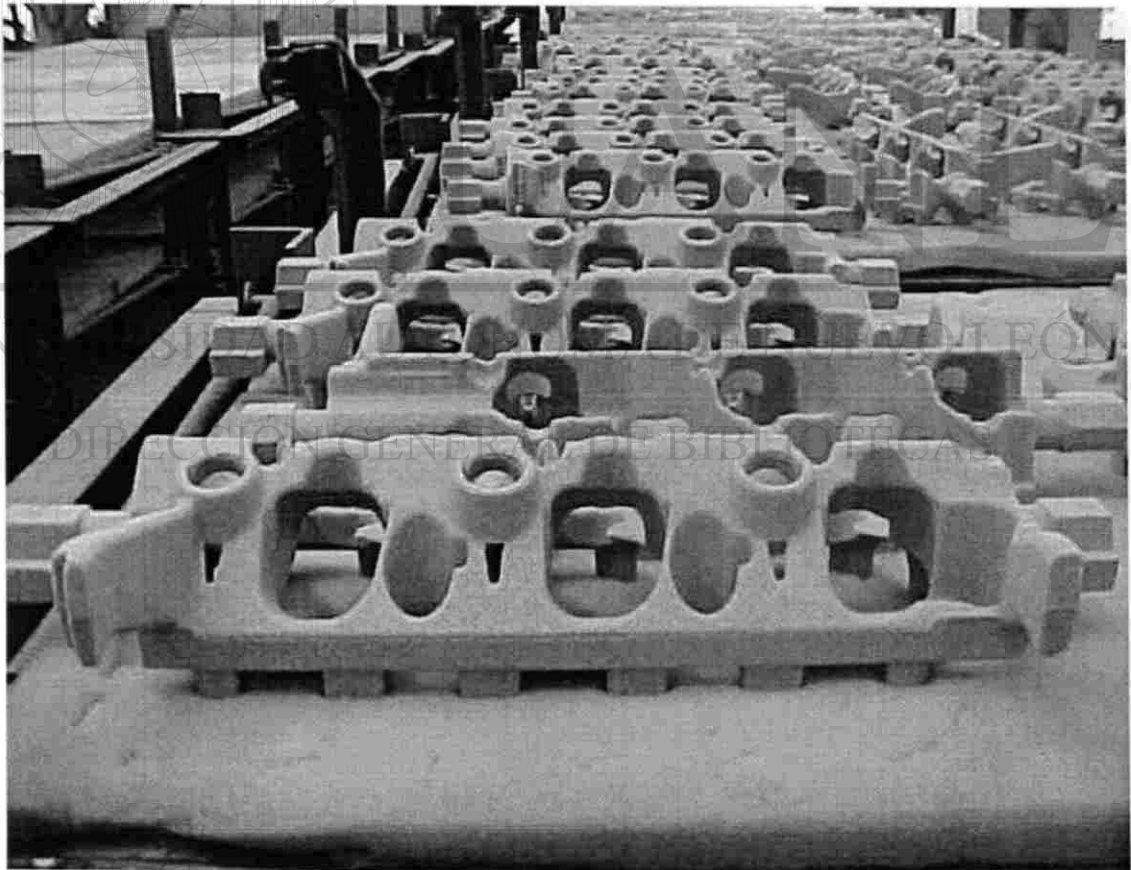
Aspecto de la chaqueta de enfriamiento de una cabeza de motor.
